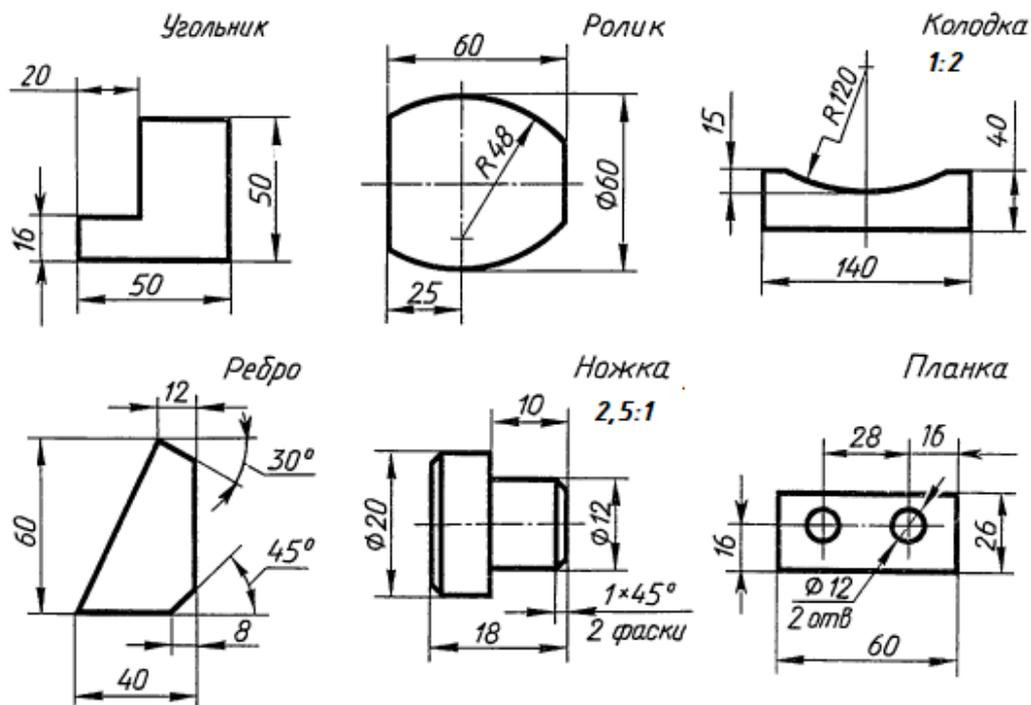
Образец графической работы «Правила нанесения размеров на чертежах» [10]
